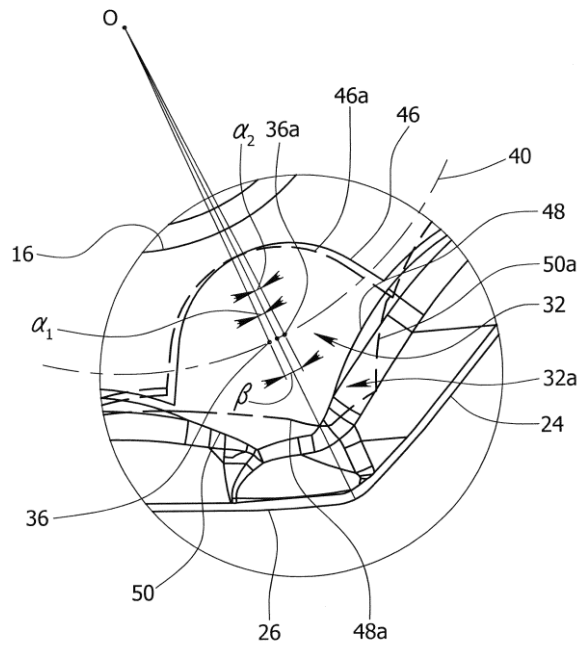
увеличенный фрагмент I вида сверху на первую поверхность для отвода стружки многогранной двухсторонней режущей пластины
